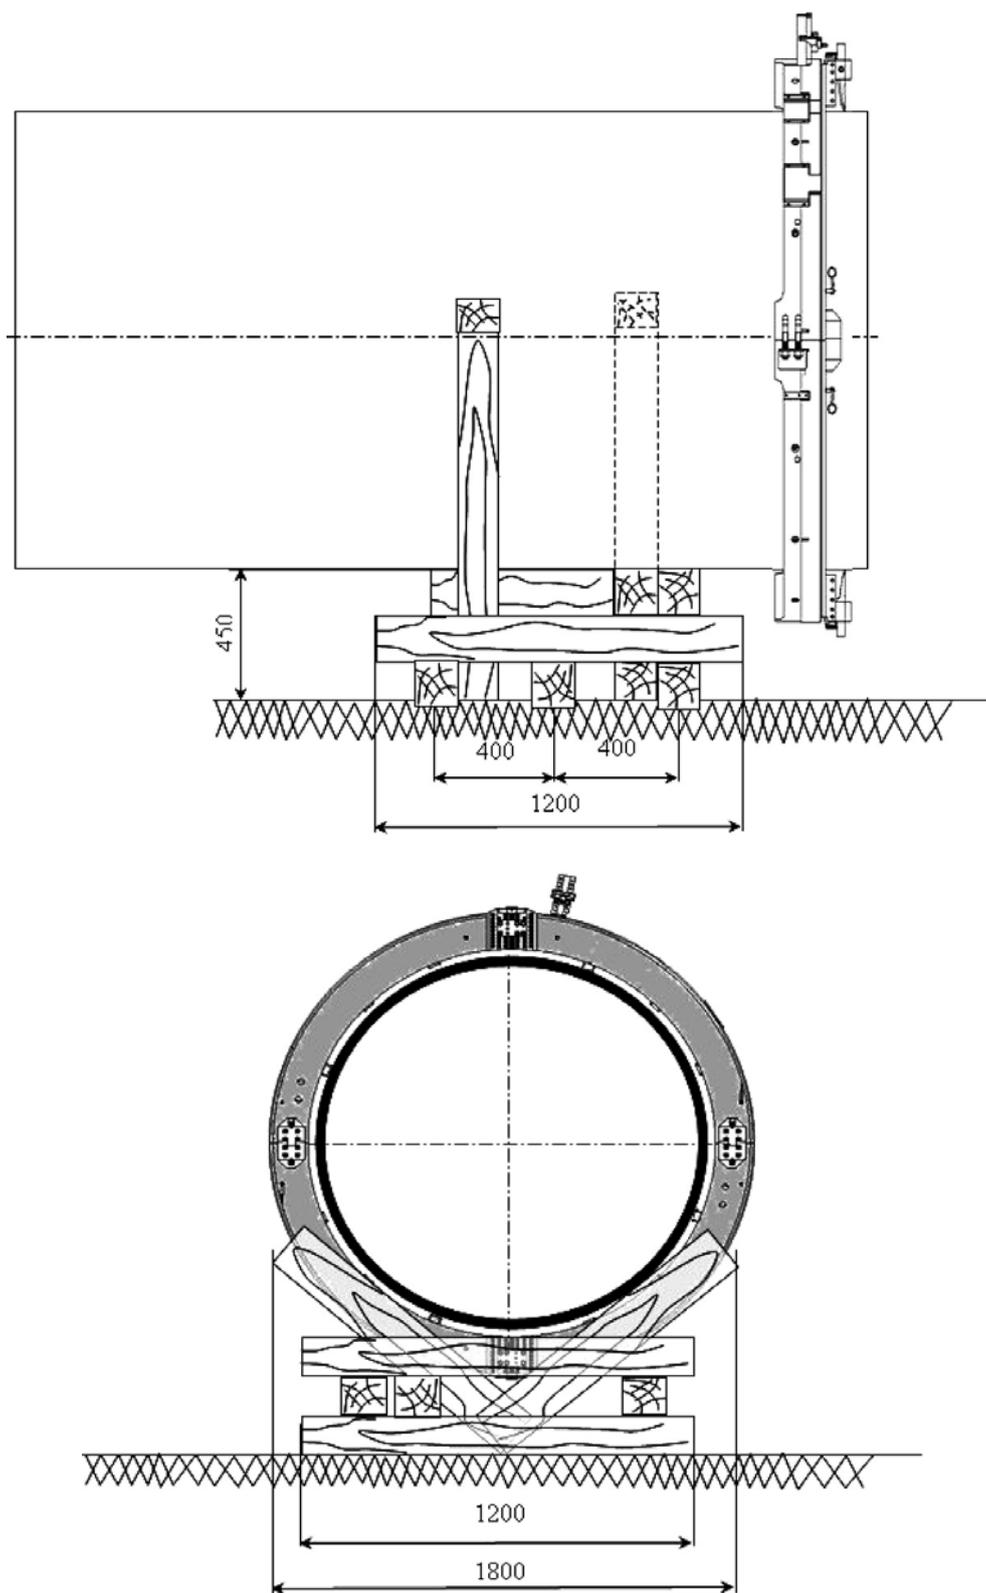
Схема укладки трубы на анкерные опоры и установки кромкообрабатывающего станка на трубе
